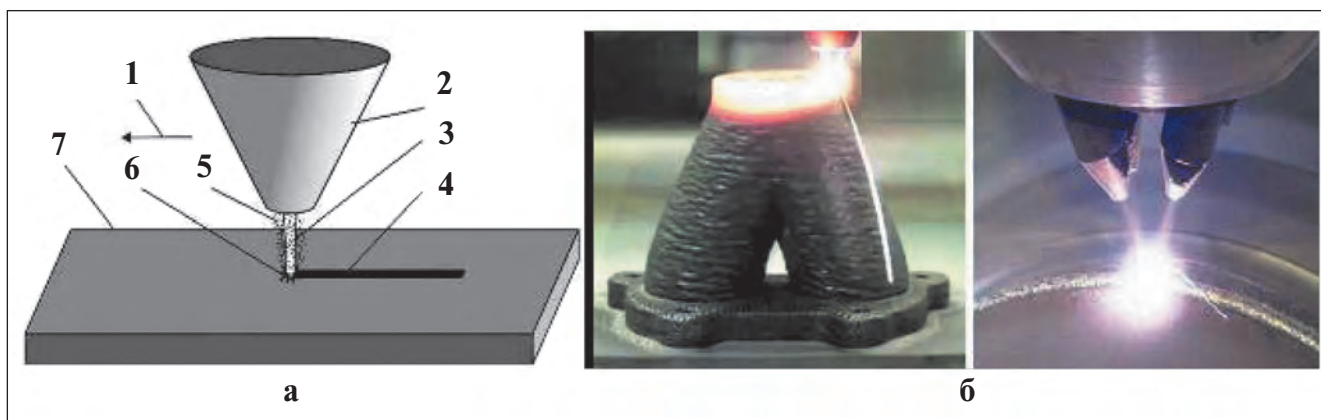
Спосіб 3D-друку металовиробів: а) принципова схема [5]; 1 — напрям руху; 2 — сопло осаджувача; 3 — пучок променів лазера; 4 — осаджений шар; 5 — частинки порошку; 6 — зона розплаву; 7 — підкладка; б) — приклади виконання
